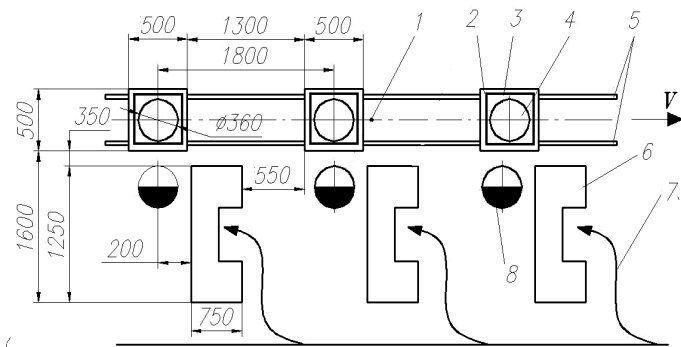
Схема планировки сборочной позиции конвейера:
